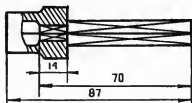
Приспособление для отворачивания пробки в блоке цилиндров «Москвича-412».
